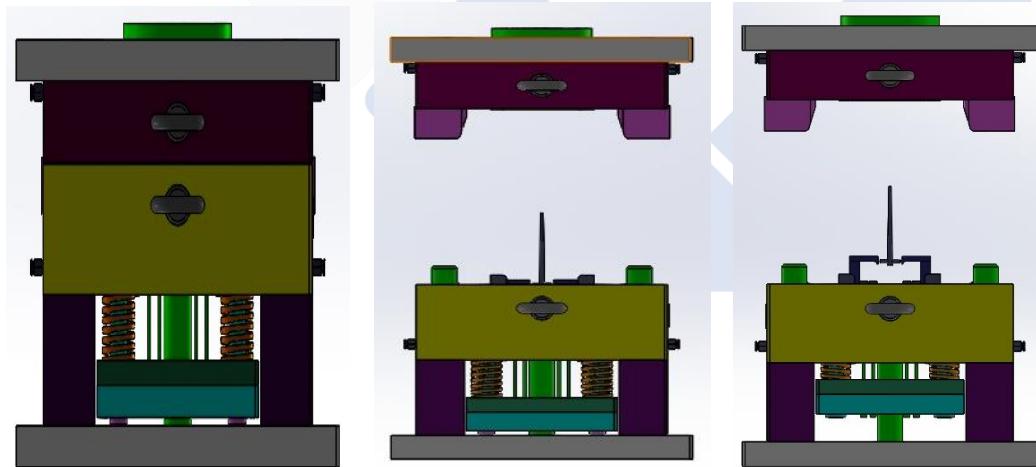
Proses Assembly Desain Cetakan Produk Holder
